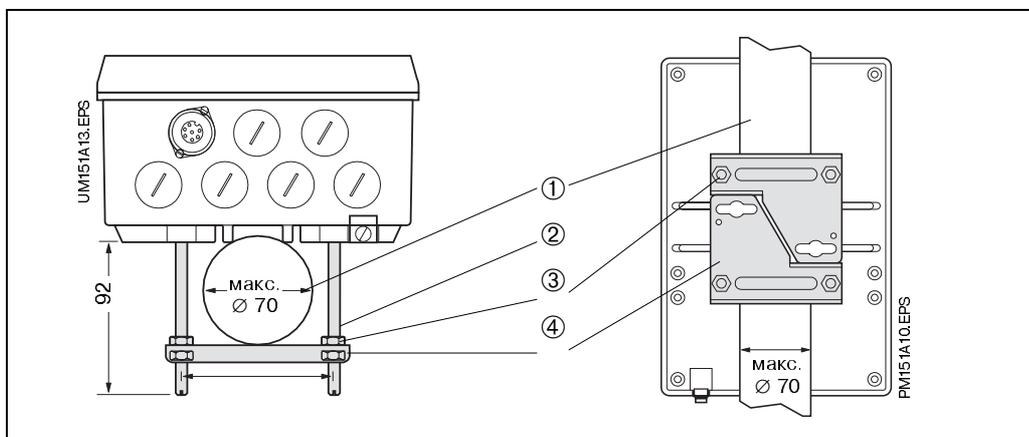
Монтаж корпуса для раздельного монтажа по месту на вертикальном участке трубопровода
